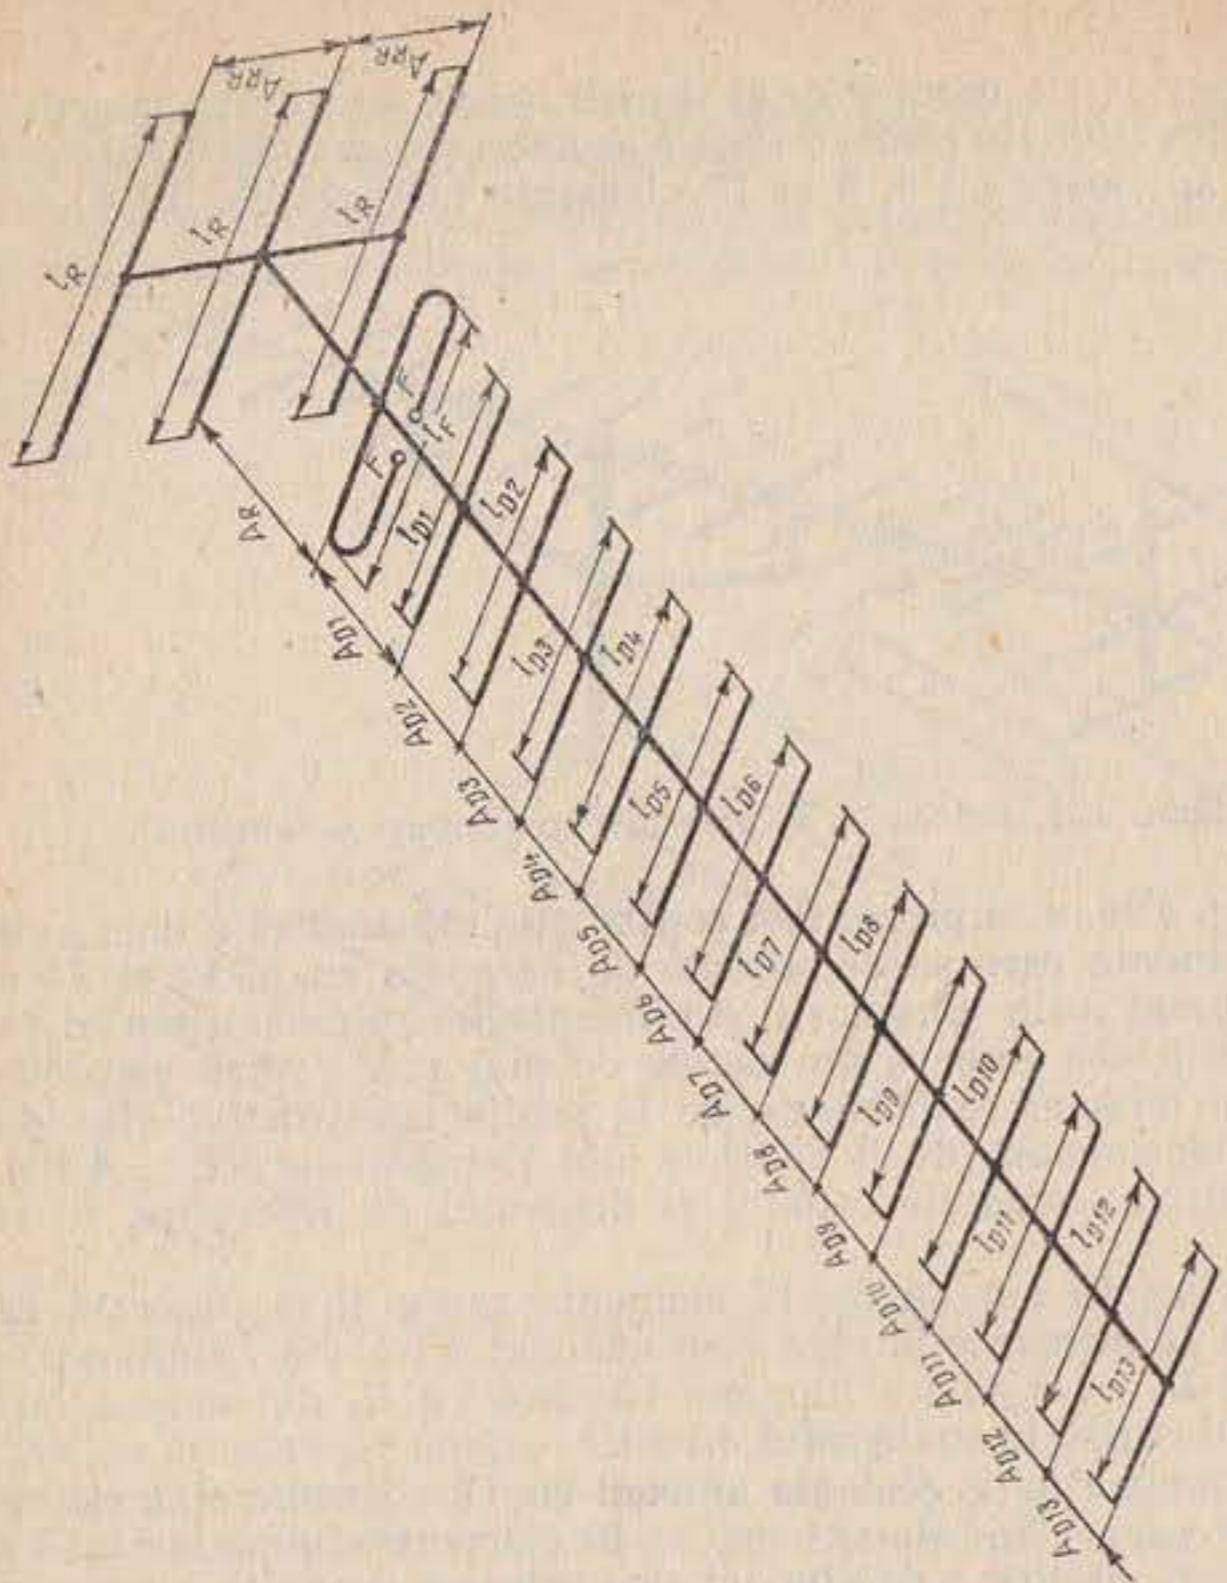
Schiță constructivă a antenei cu 17 elemente.
